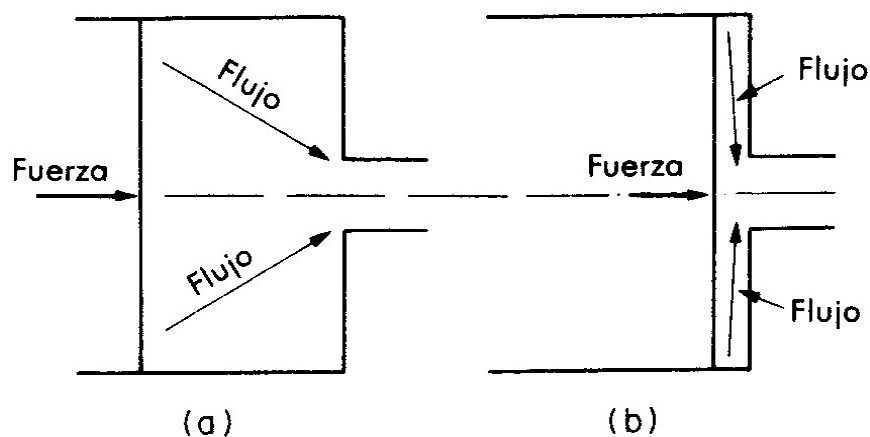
Esquema del flujo y la fuerza en un proceso de extrusión.
